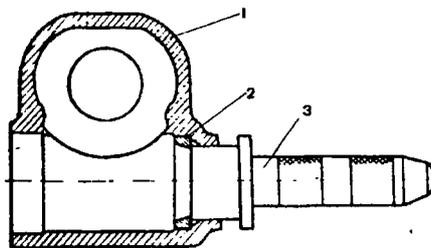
Снятие наружного кольца верхнего подшипника червяка с помощью съемника 67.7853.9541: 1 - картер рулевого механизма; 2 - наружное кольцо верхнего подшипника червяка; 3 - оправка 67.7853.9541
